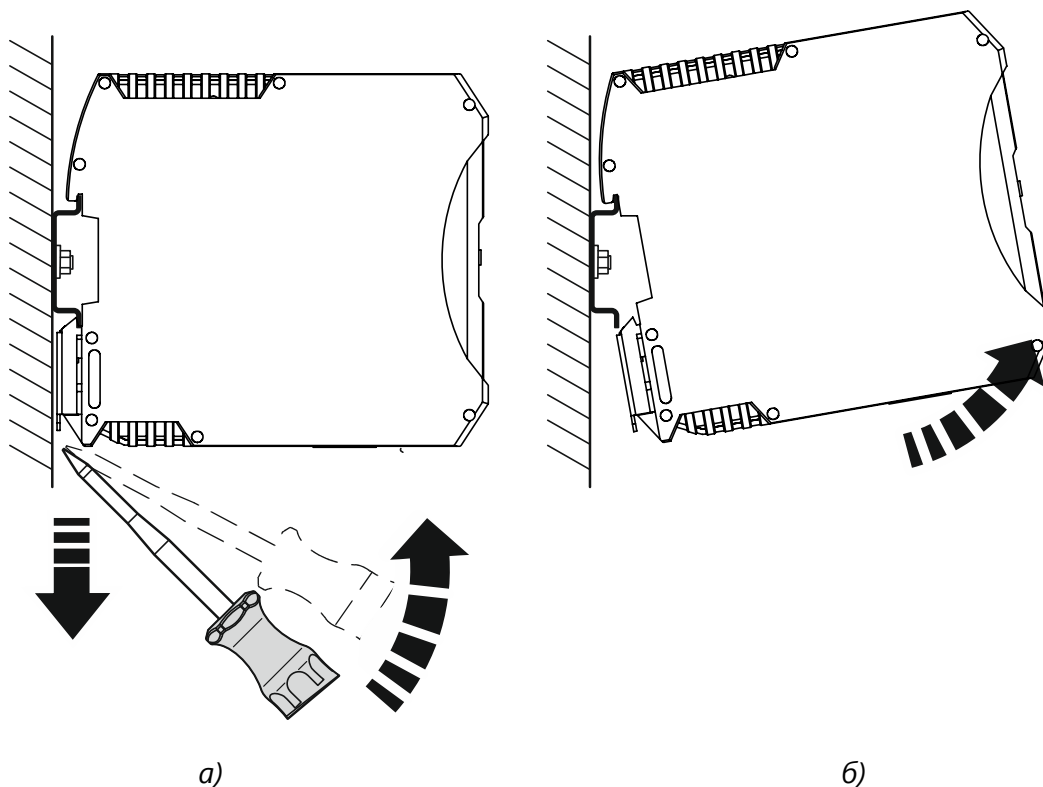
Снятие IPN-1LE с DIN-рейки
